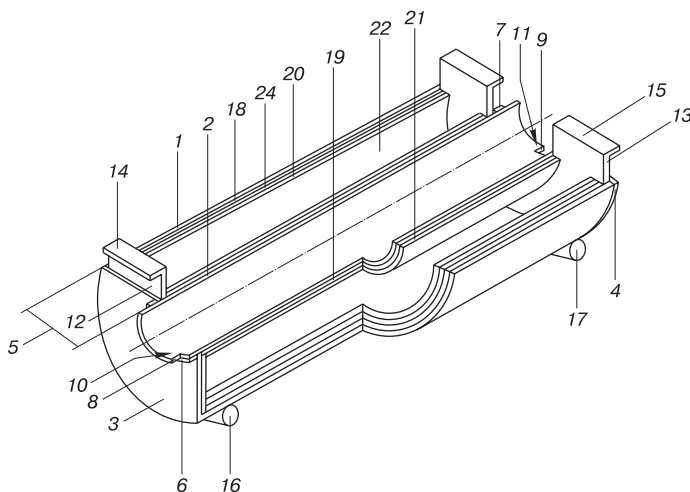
Конструктивная схема формы для изготовления скорлуп из газобетона
